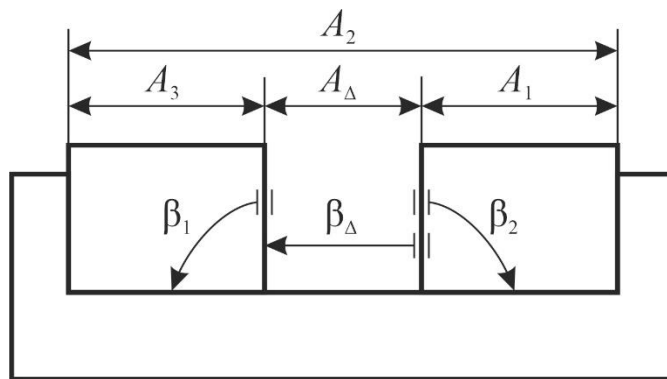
Схема линейных, угловых размеров и обозначение звеньев
